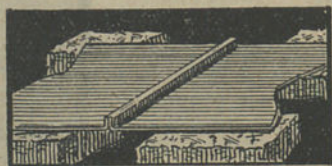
Soldadura de chapas muito delgadas com bordos levantados.
